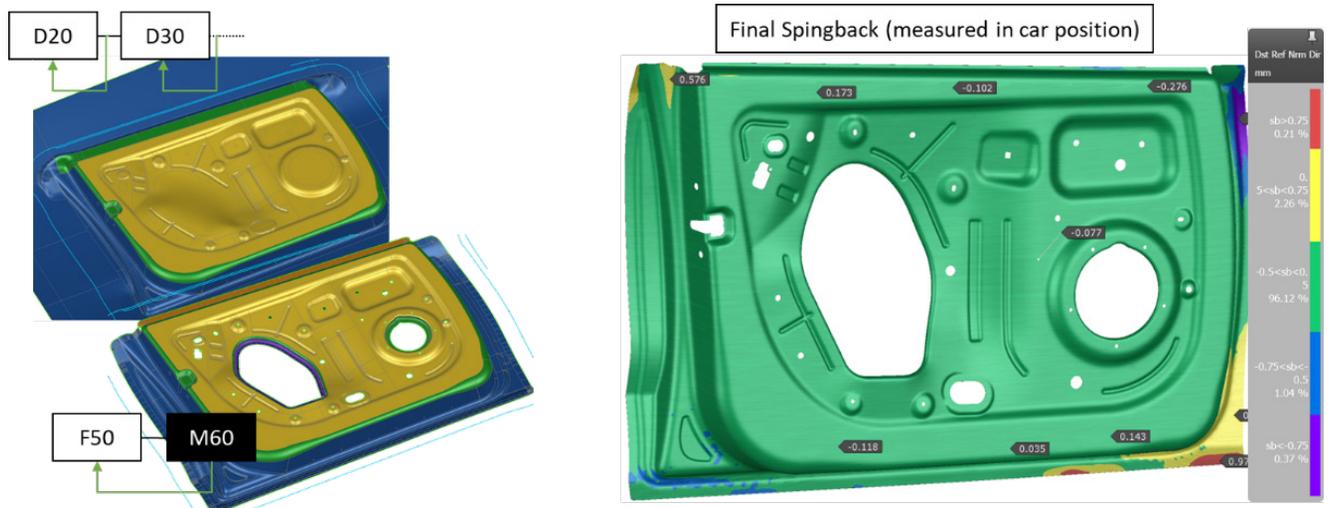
Compensação do Ferramental e Resultado Dimensional
